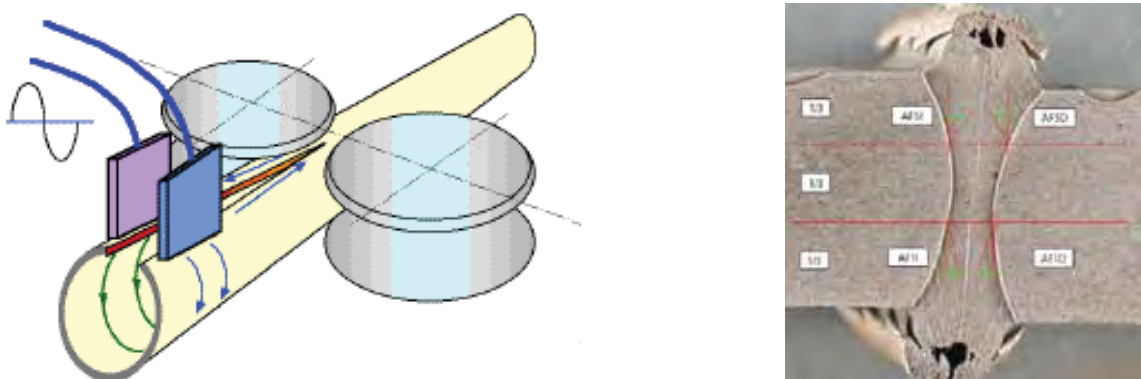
Representação esquemática da solda ERW (EQUIPE USIMINAS; 1988)
